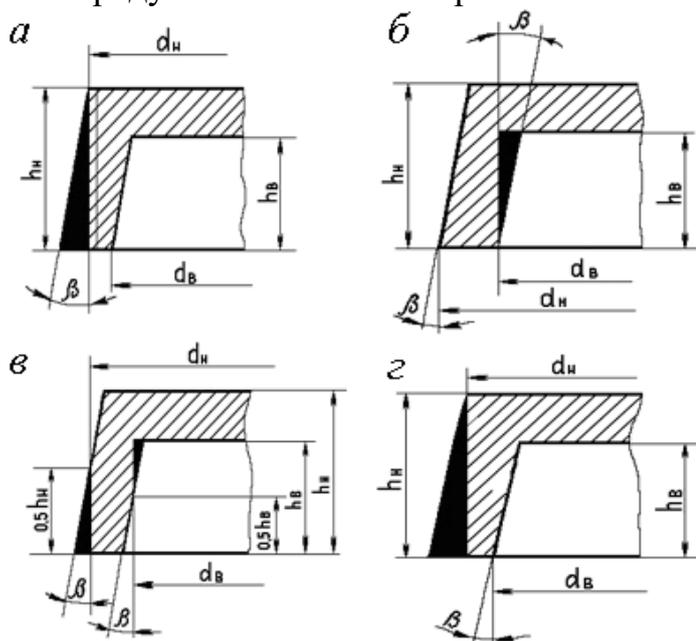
Формовочные уклоны: а – на обрабатываемых поверхностях отливки сверх припуска на механическую обработку за счет увеличения размеров отливки; на необрабатываемых поверхностях отливки: б – за счет одновременного увеличения и уменьшения размеров; в – за счет уменьшения размеров; г – за счет увеличения размеров
